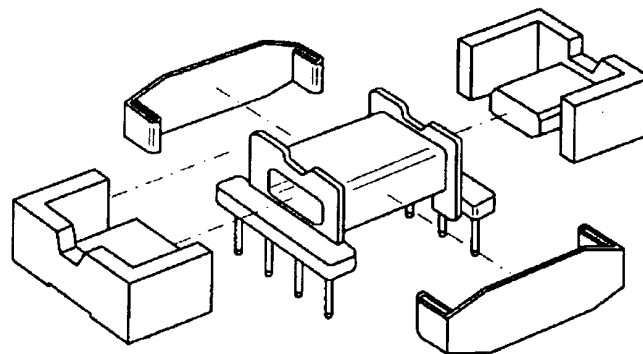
Explosionszeichnung des besonders für Flachbauweise geeigneten Kerntyps EFD
